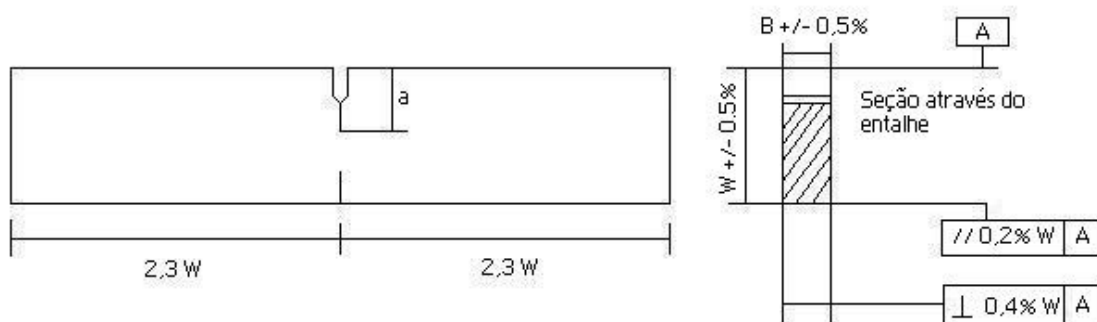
Vista frontal do corpo de prova SE(B) de seção retangular [7]
